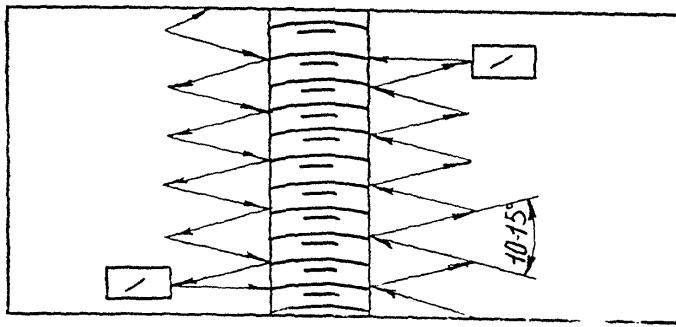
Схема перемещения искателя по поверхности при контроле сварного шва
